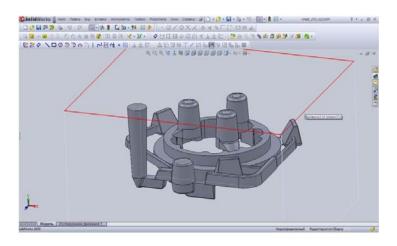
Трёхмерная модель отливки «Колесо»
